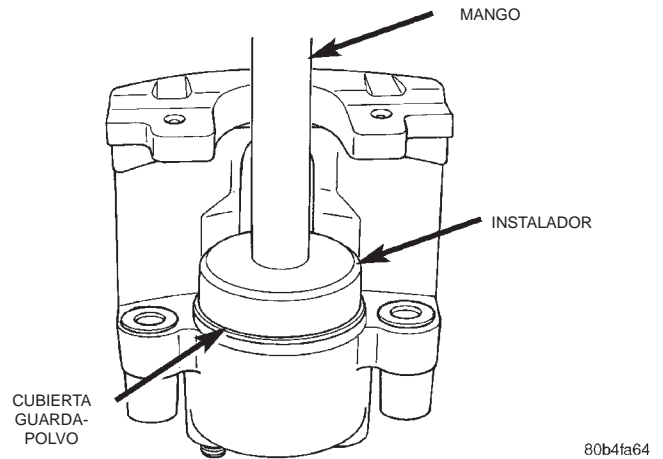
Instalación de la cubierta guardapolvo del pistón
